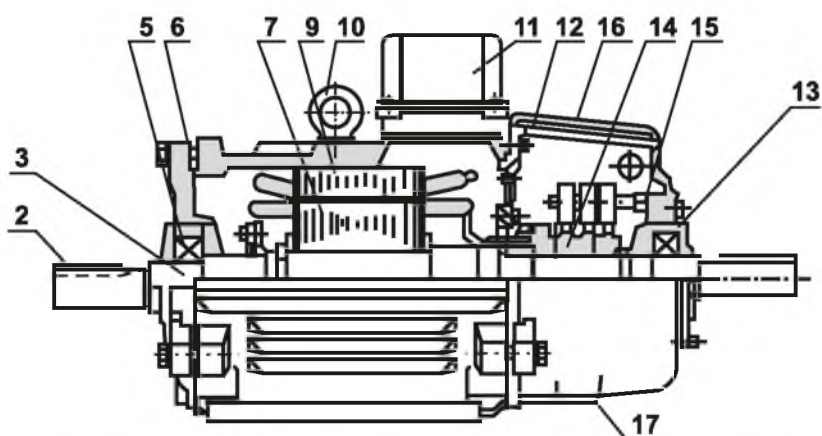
Конструкция электродвигателя с фазным ротором без дополнительной вентиляции (самоохлаждающийся)
